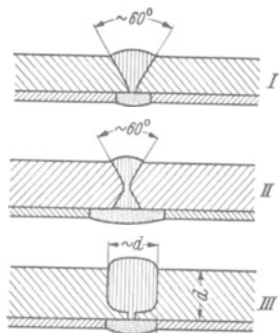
Vorbereitung und Schweißung plattierter Bleche.
